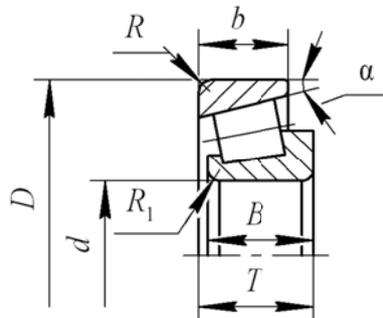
Габаритные размеры роликовых конических однорядных подшипников
